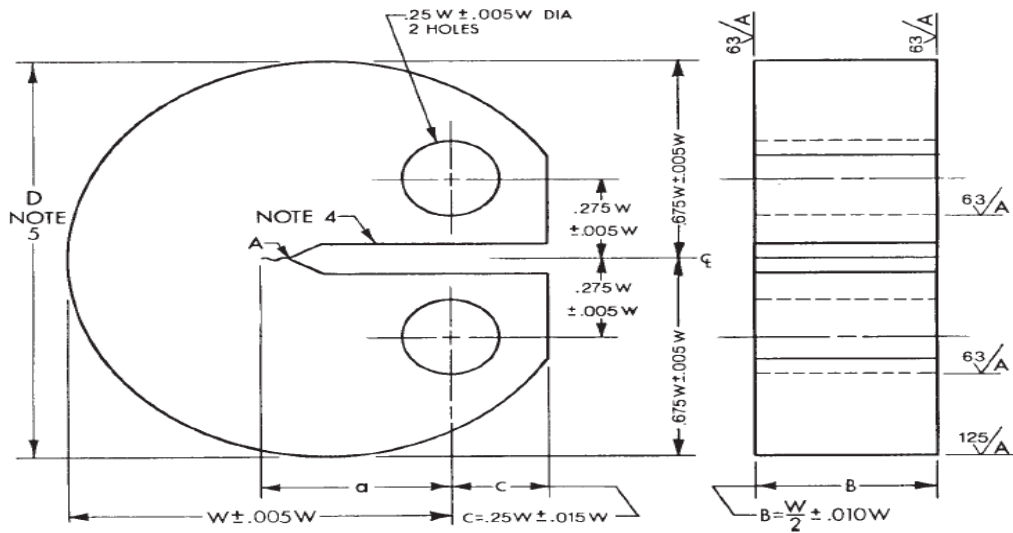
Dimensiones de la probeta de latón para el ensayo de corrosión bajo tensión
